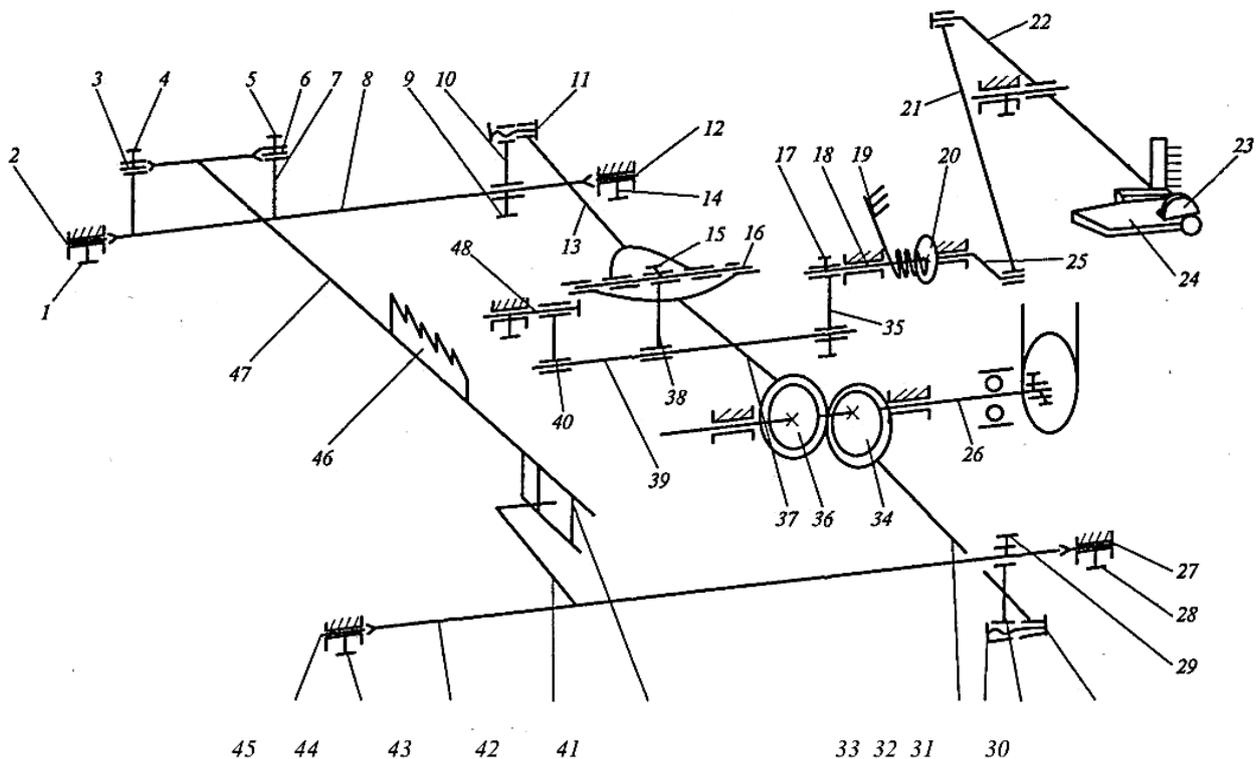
Кинематическая схема механизма перемещения рейки
